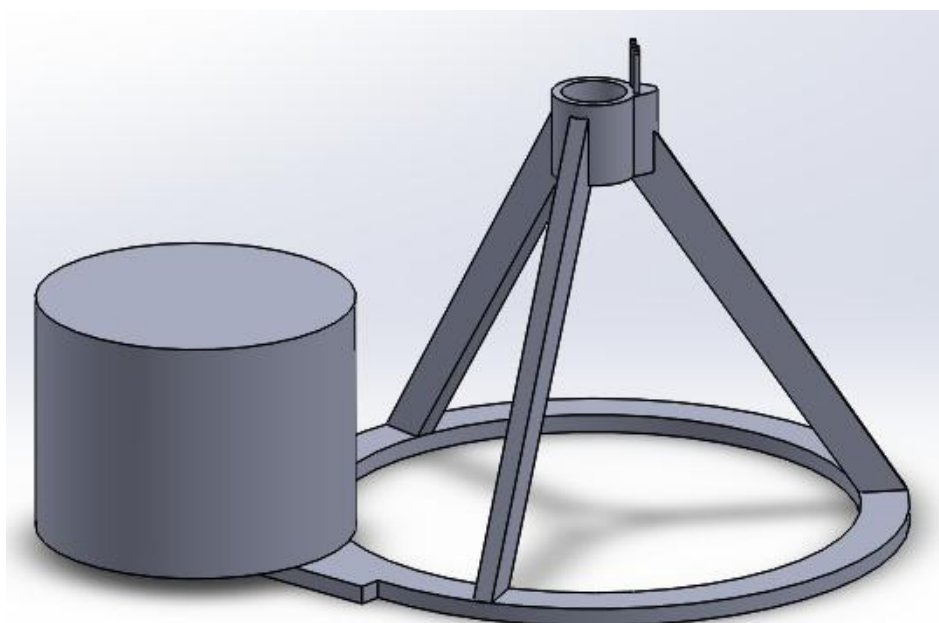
3: Pie de la estructura de extracción anti vuelco con su bloque de hormigón.
